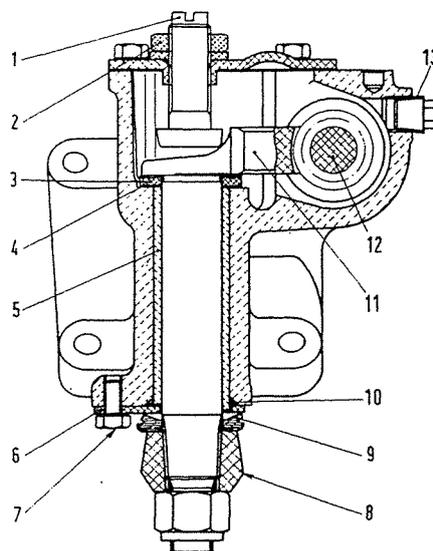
Schnitt des Lenkgehäuses durch das Lenksegment.
